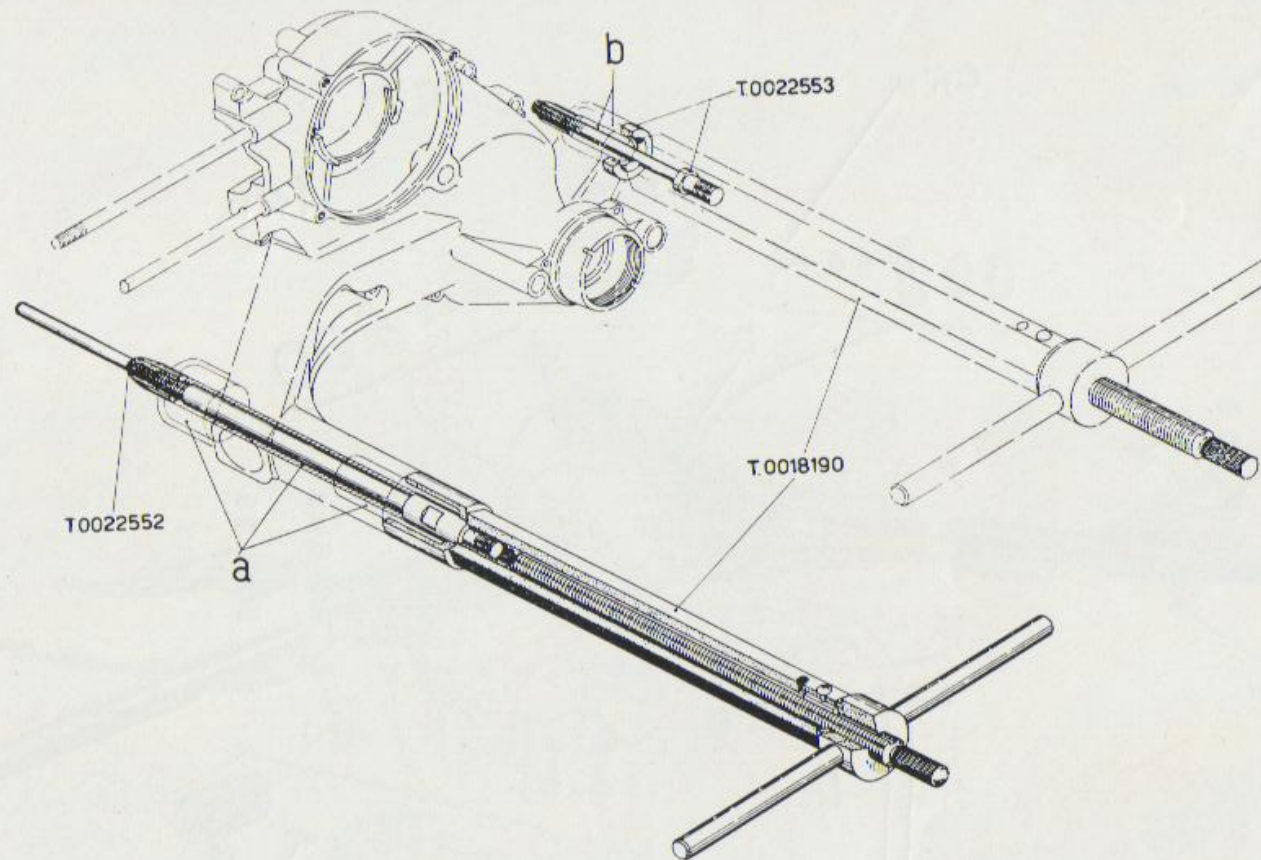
a) Pièce de fixation du moteur à la coque.
